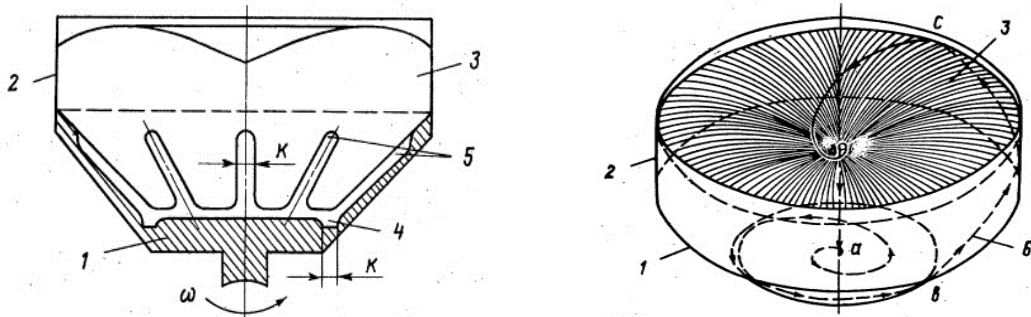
Відцентрова установка для абразивної поверхневої обробки заготовок:
